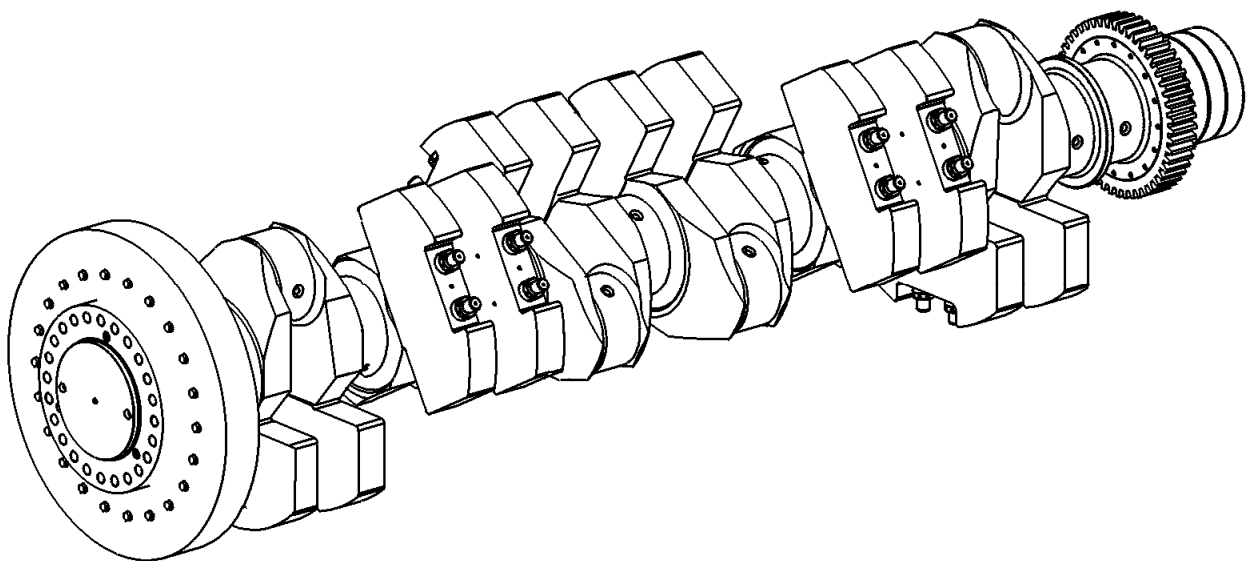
Колінчатий вал двигуна М 43С
